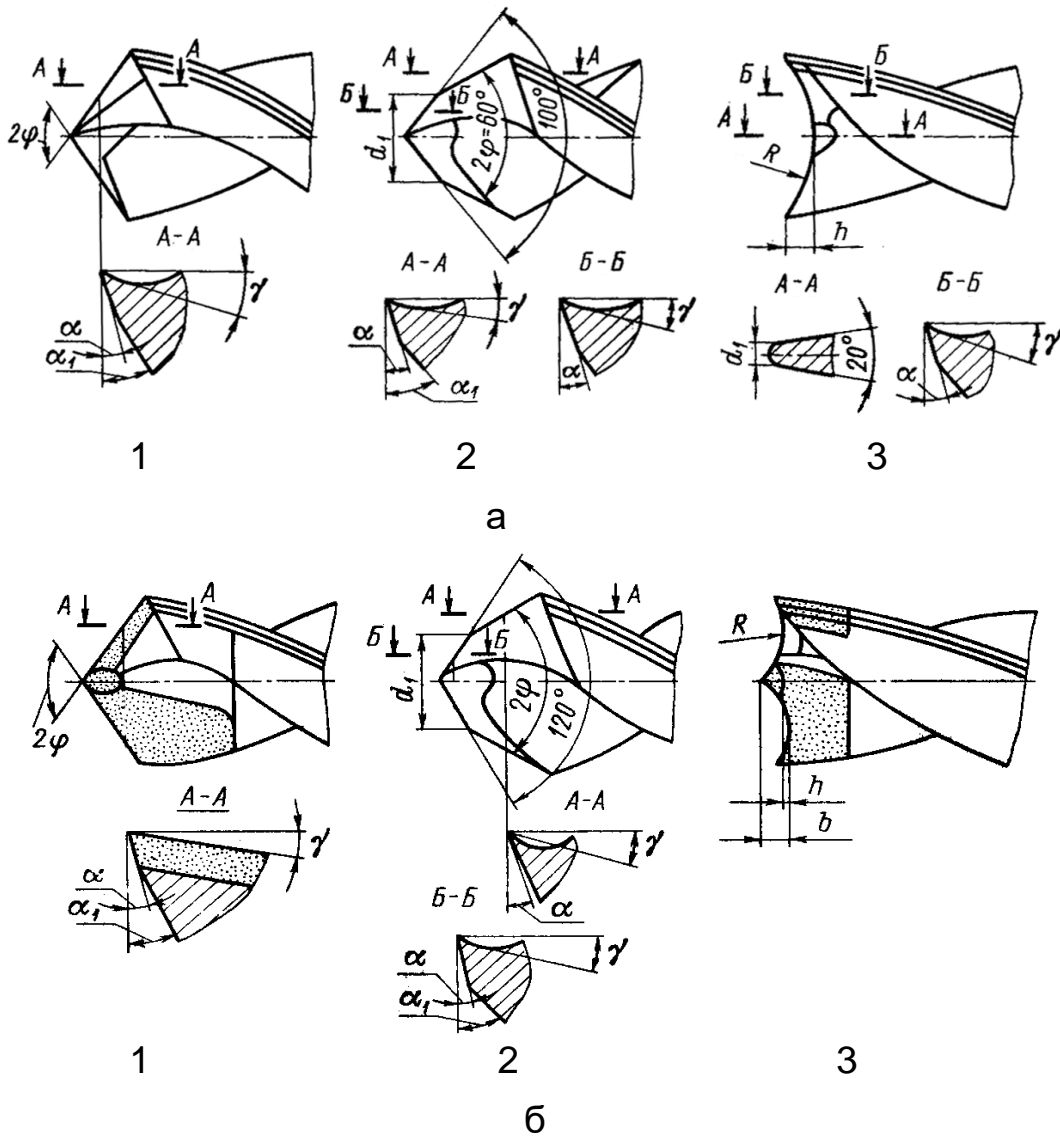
Формы заточки режущей части сверл из быстрорежущих сталей (а) и твердых сплавов (б):
